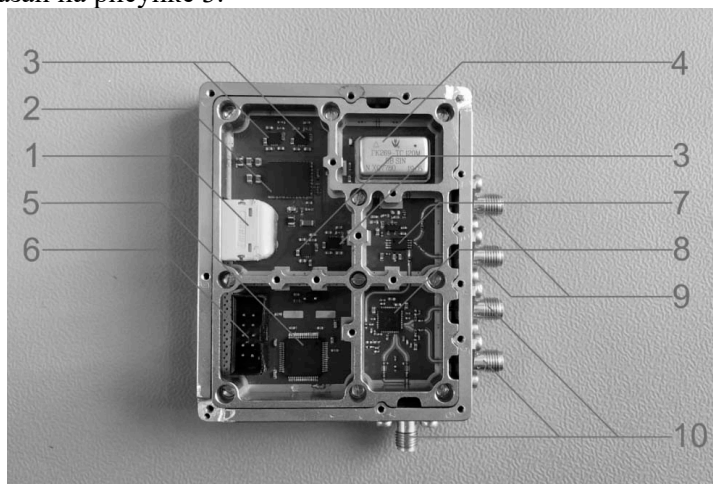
Внешний вид блока в корпусе без крышки. Цифрами обозначены:
